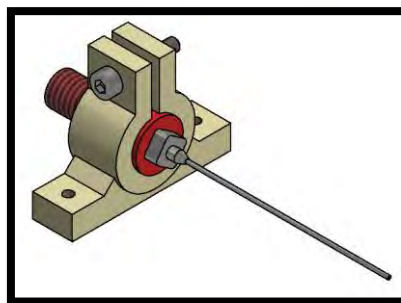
Soporte impreso en 3D para conector Luer Lock con aguja eyectora
